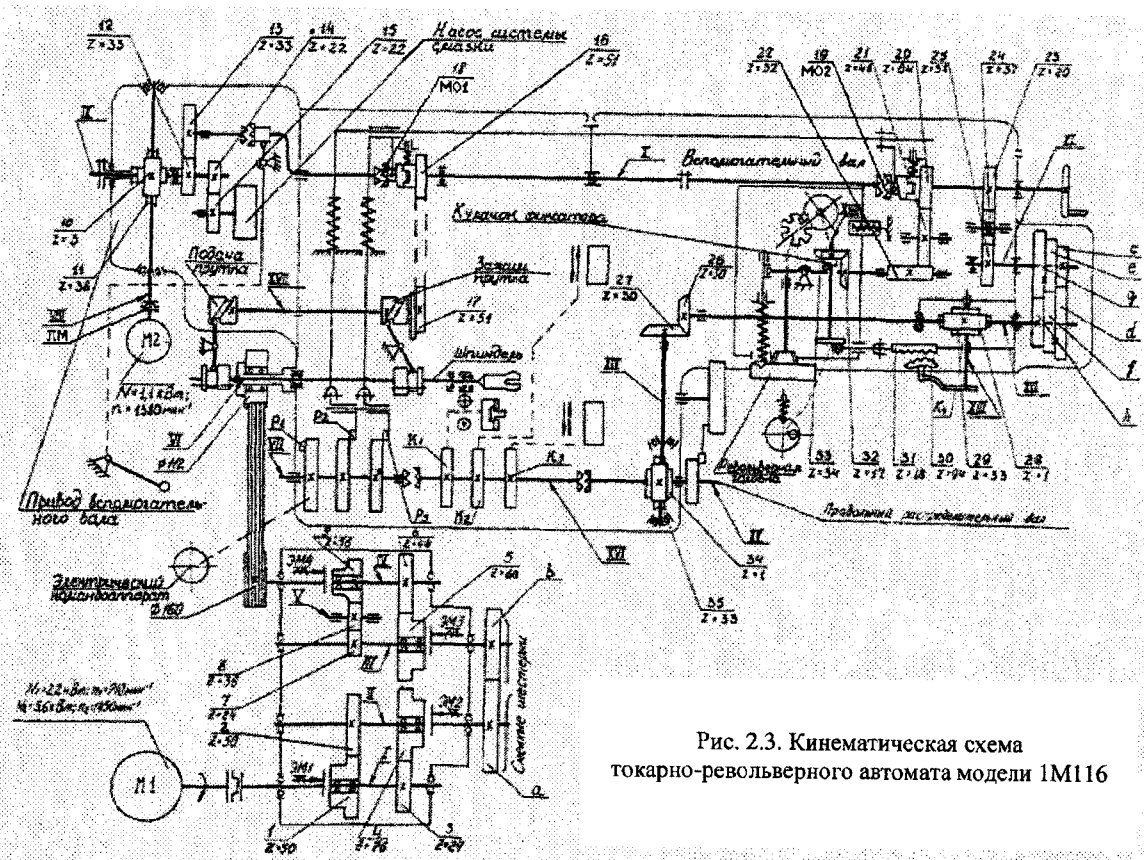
Кинематическая схема токарно-револьверного автомата модели 1M116
